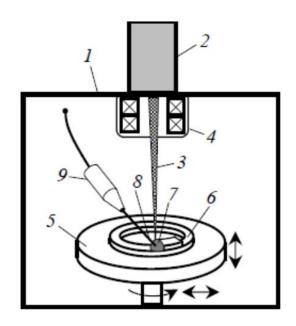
Схема установки электронно-лучевого выращивания: 1 - вакуумная камера; 2 - электронный источник; 3 - электронный пучок; 4- Система магнитной фокусировки; 5 - подложка; 6 - предыдущий наплавленный слой; 7- ванна расплава; 8- подаваемая проволока; 9 - манипулятор подачи проволоки; стрелками показаны направления смещения подложки.
